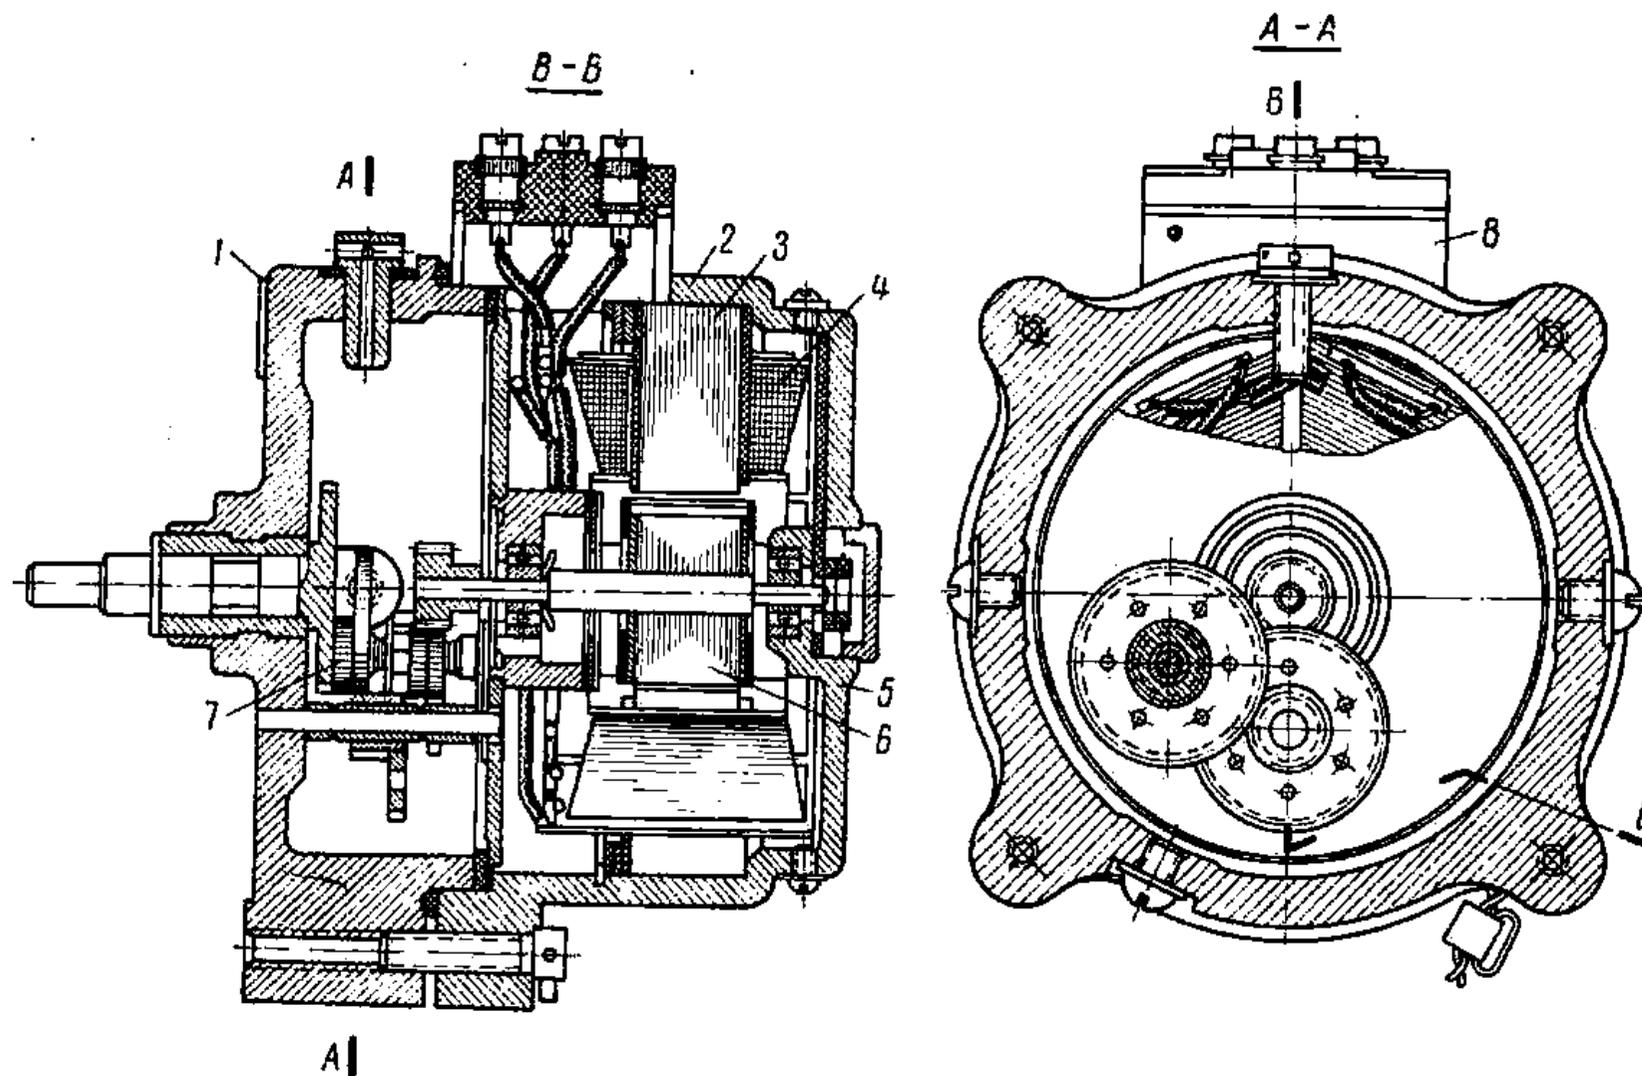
Общий вид и разрез электродвигателя серии СД: 1 – крышка редуктора; 2 – корпус; 3 – сердечник статора; 4 – обмотки статора; 5 - подшипниковый щит; 6- ротор; 7 – редуктор; 8 – коробка выводов
